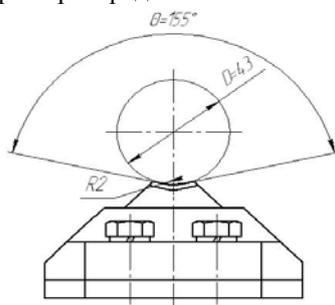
Внешний вид деформирующего инструмента  $\square$  – угол охвата заготовки.
